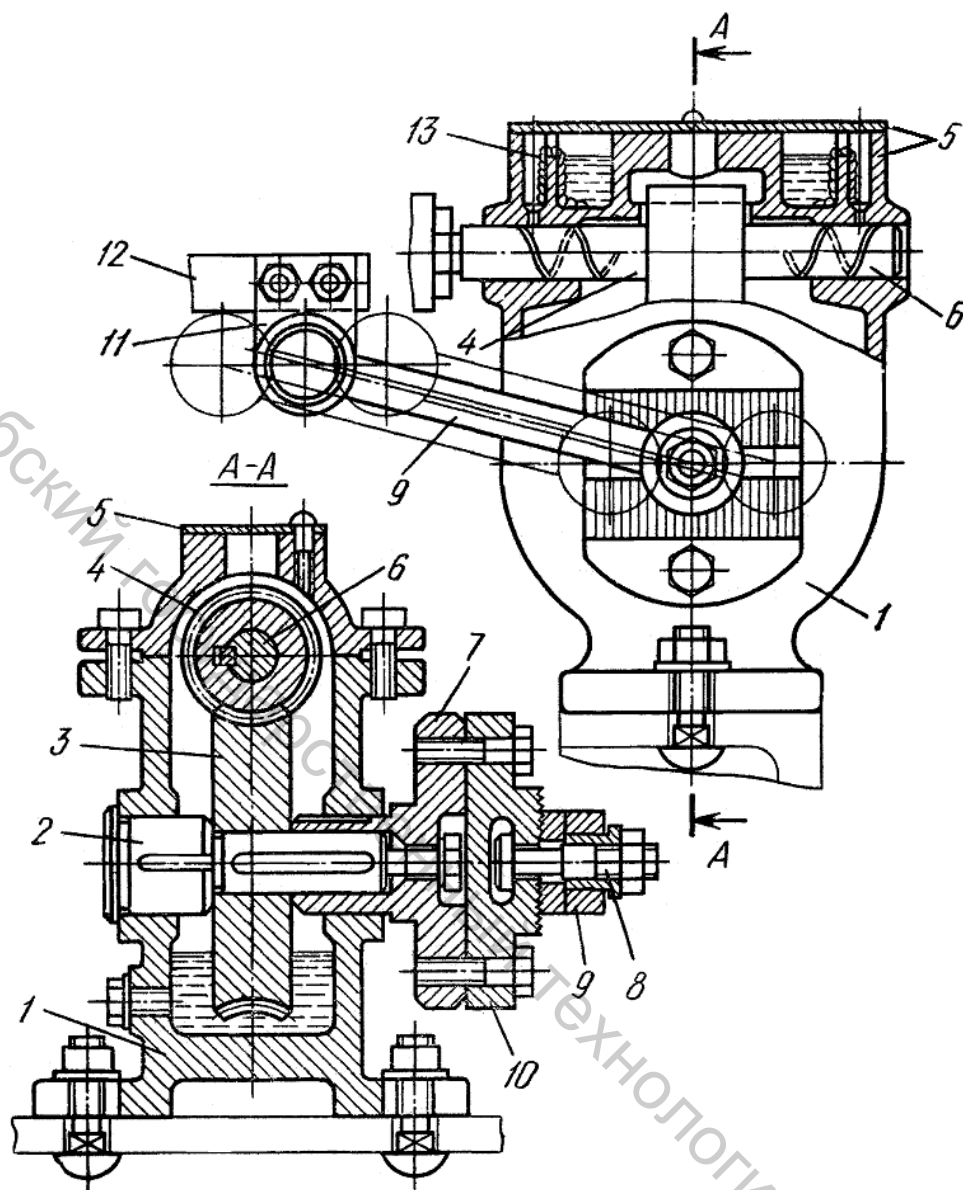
Механизм передачи движения водилке кольцевых крутильных машин тяжелого типа К-132-2
